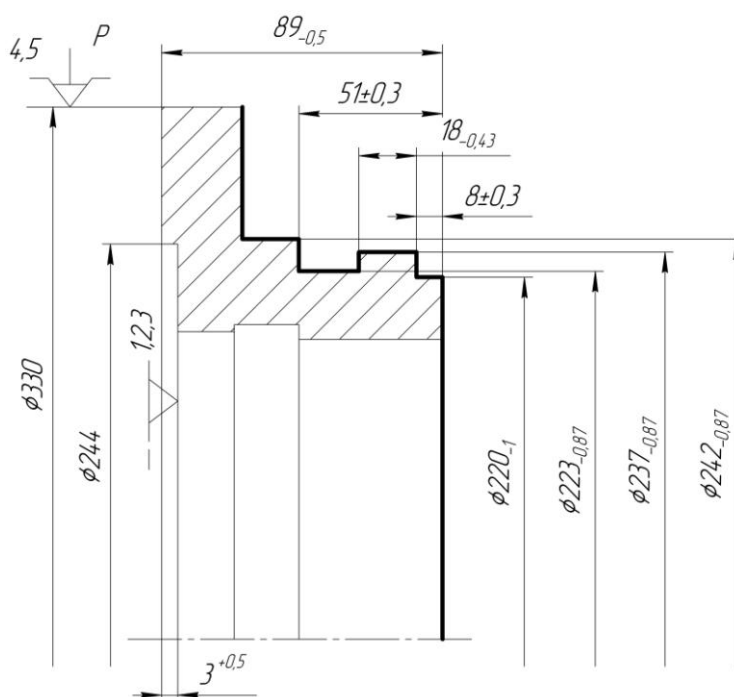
Схема базирования заготовки на токарной с ЧПУ операции (первый вариант)
